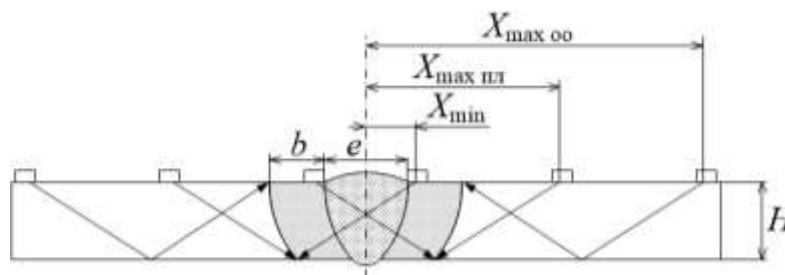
Схема контроля стыкового сварного соединения.
